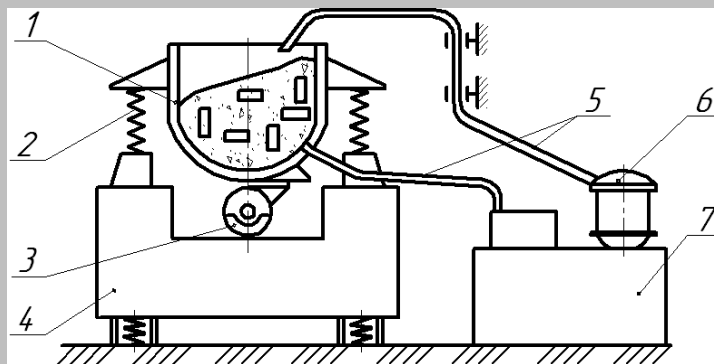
Схема процесса вибрационной обработки: 1 - рабочая камера; 2- пружины; 3 - дебалансный вибратор; 4 - основание; 5 - шланги для подачи и слива СОТС; 6 - помпа; 7 - бак-отстойник.
